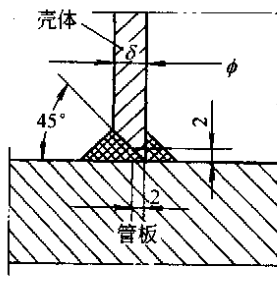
管板与壳体焊接 ($DN > 600$)
